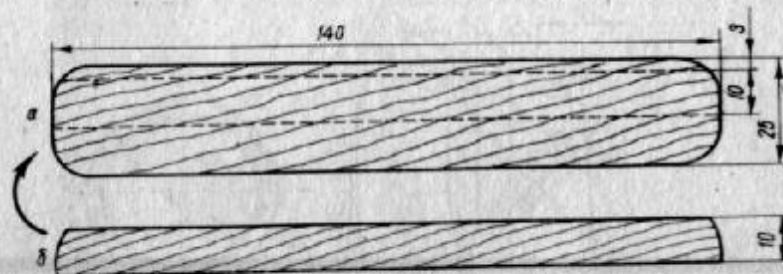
Шпонові заготовки для лопатей ротора (деталь б наклеюють на деталь а в місці, позначеному пунктиром).
